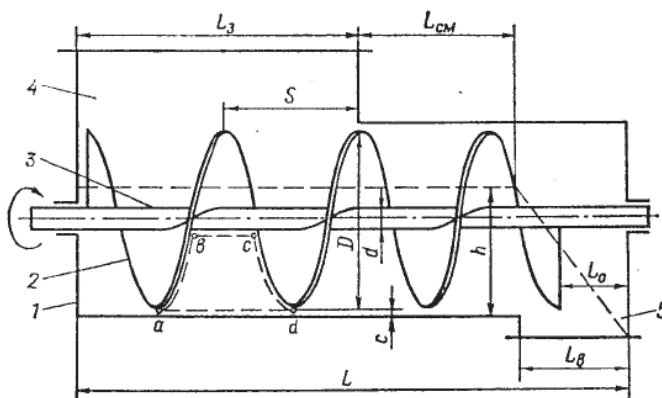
Розрахункова схема шнекового дозатора: 1 – жолоб; 2 – гвинтова лопать; 3 – вал; 4 – прийомний патрубков; 5 – вихідний патрубков
